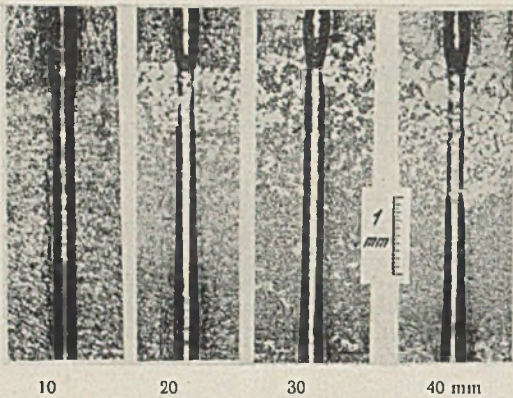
Abrollbahnen der Prüfkugel des Rollhärteprüfers über die Schweißnaht eines 10, 20, 30, 40 mm dicken unlegierten Kohlenstoffstahls.
